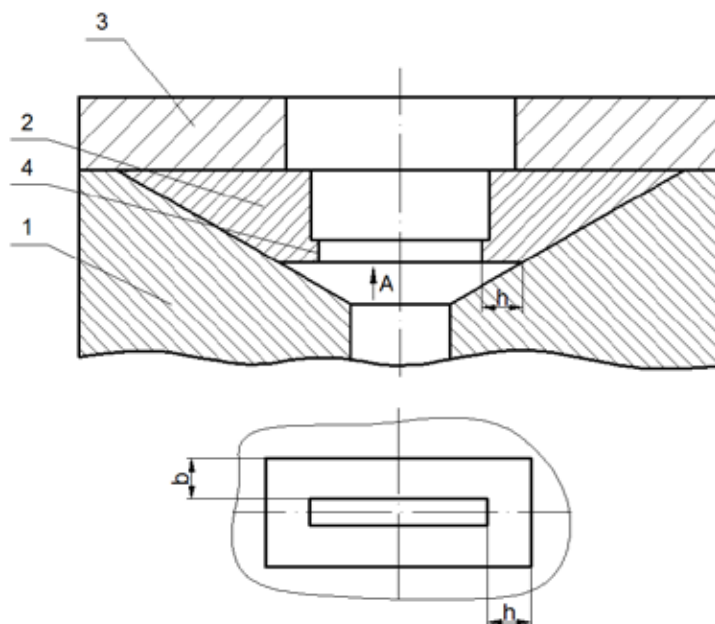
Схема расположения матрицы в расширяющейся форкамере: 1 – форкамера; 2 – матрица; 3 – опора; 4 – калибрующий поясok матрицы
